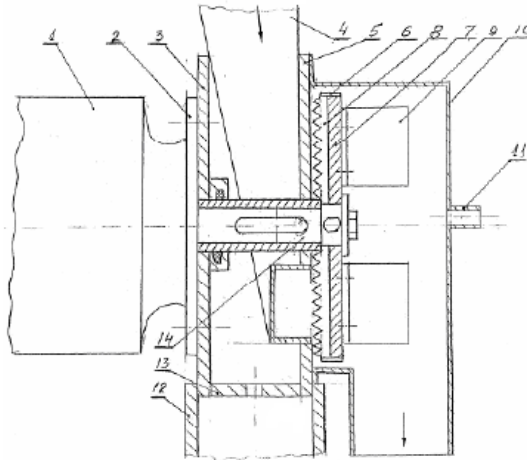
Загальний вигляд селективної дробарки: 1 – електродвигун-рушій; 2 – фланець двигуна; 3 – корпус; 4 – бункер-завиток; 5 – проміжний диск; 6 – лопатки диска дробарки; 7 – зубчасті ножі; 8 – диск; 9 – лопатки-вивантажувачі; 10 – збірник рослинної пульпи; 11 – патрубок для подачі пари; 12 – станина; 13 – перемичка дисків; 14 – вал розташований горизонтально
